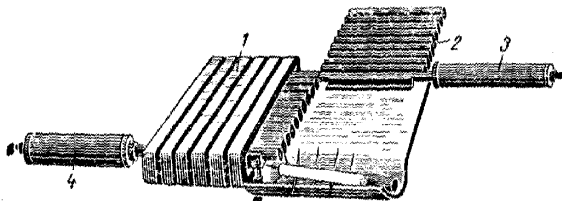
Схема нагревателя для нагрева концов, длина которых в несколько раз больше их диаметра: 1 — индуктор; 2 — магазин с заготовками; 3 — заталкиватель заготовок; 4 — выталкиватель заготовок.
